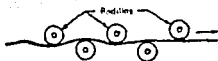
Método de enderezado de barras pasaditas a través de un conjunto de rodillos enderezadores. Rodillos que no se muestran, proveen el enderezado en la 3ª dimensión.
